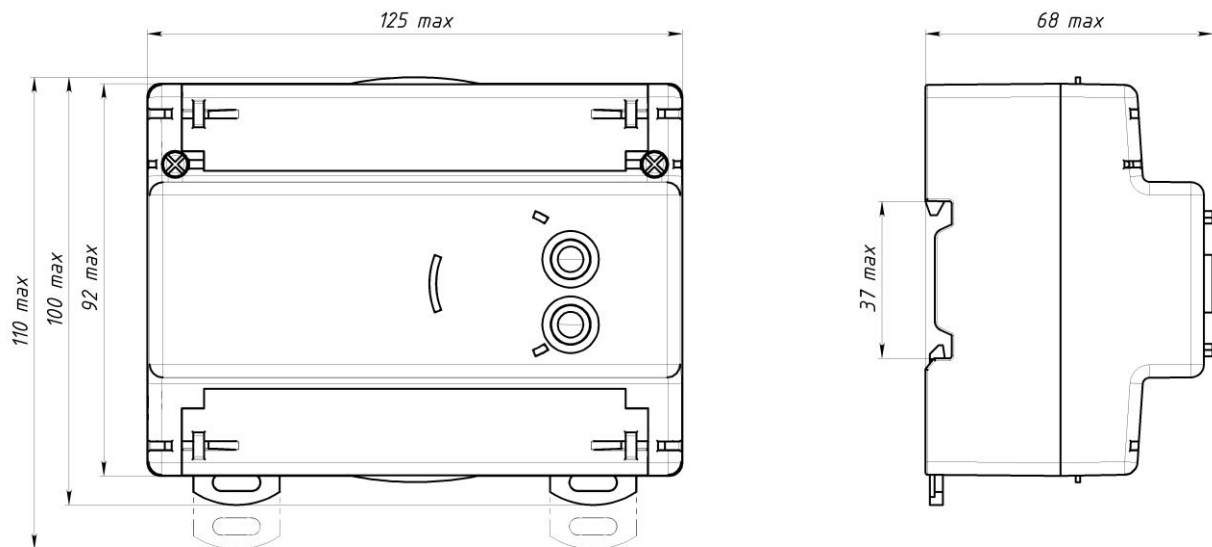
а – Корпус 7мТН35 с уменьшенными клеммными крышками
